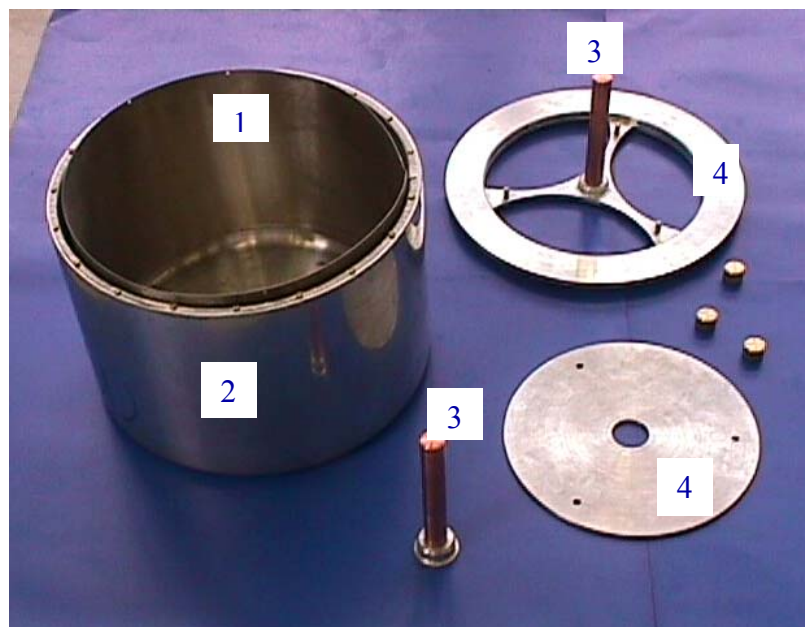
Partes da construção do transdutor *shunt*: (1) parte interna construída com Nikrothal; (2) parede externa composta de alumínio; (3) hastes de cobre; (4) tampa de alumínio.
